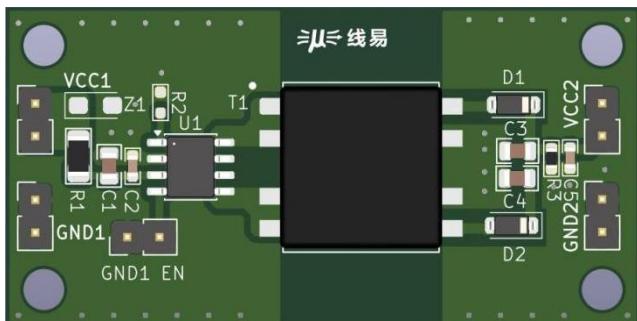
PCB 版图正面 (尺寸: 25x 50mm)
